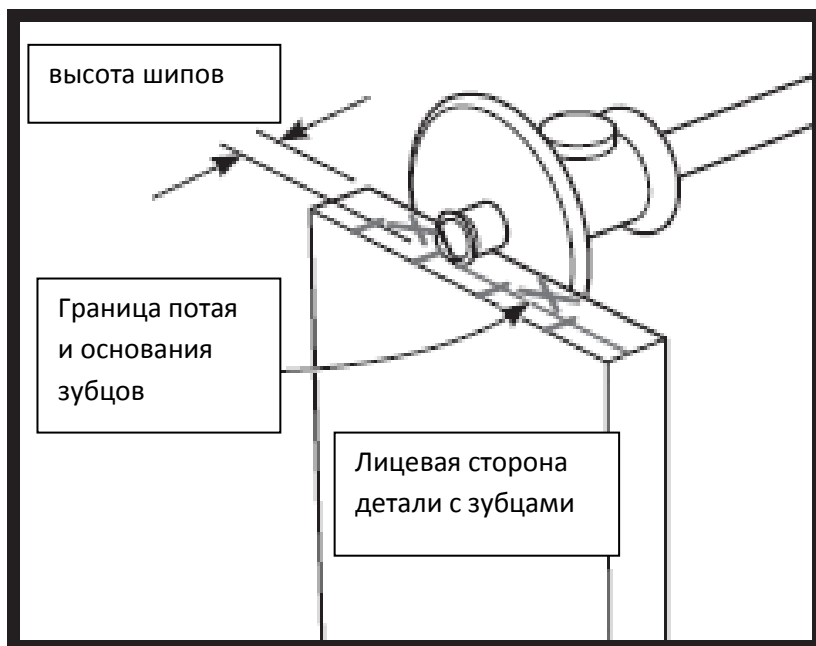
разметка рейсмасом основания зубцов на детали с зубцами. Внимание: вылет рейсмаса установлен по длине шипов на ответной детали!
